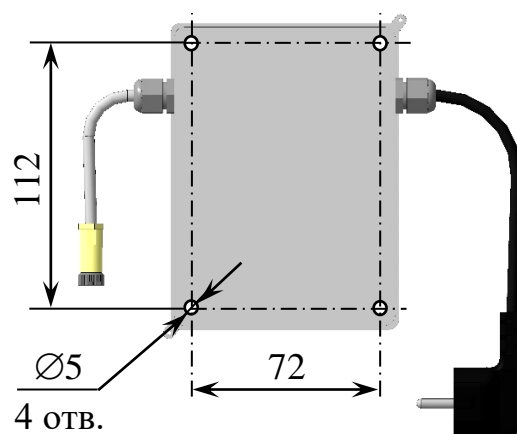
Расположение отверстий для крепления источника питания ИП-1002
